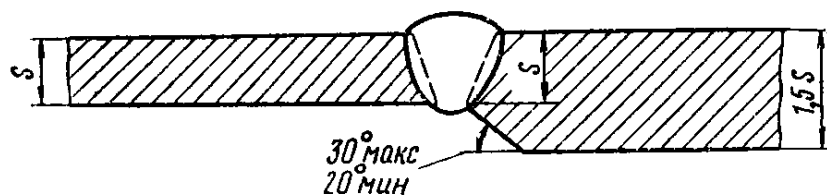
Конструктивные размеры разделки кромок и сварных швов разнотолщинных труб (до 1,5 толщины стенки)
